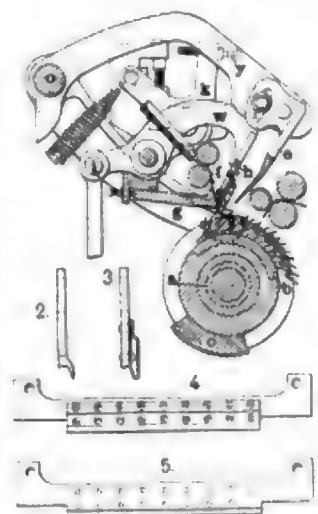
Z. A.: Oberzangen für Kämmaschinen
